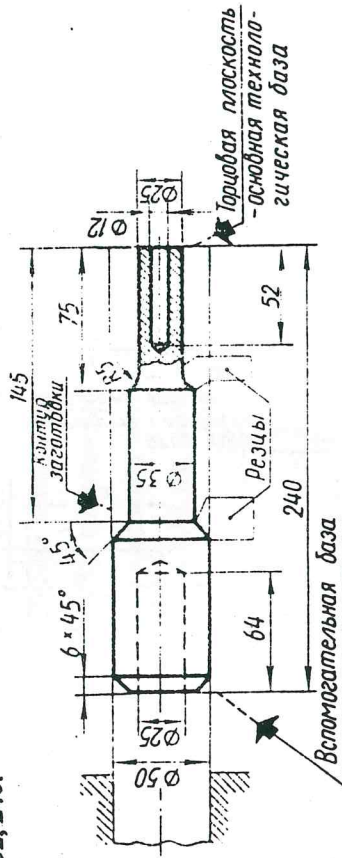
Размерные базы - торцовые плоскости на примере чертежа типовой «круглой» детали (валик).
